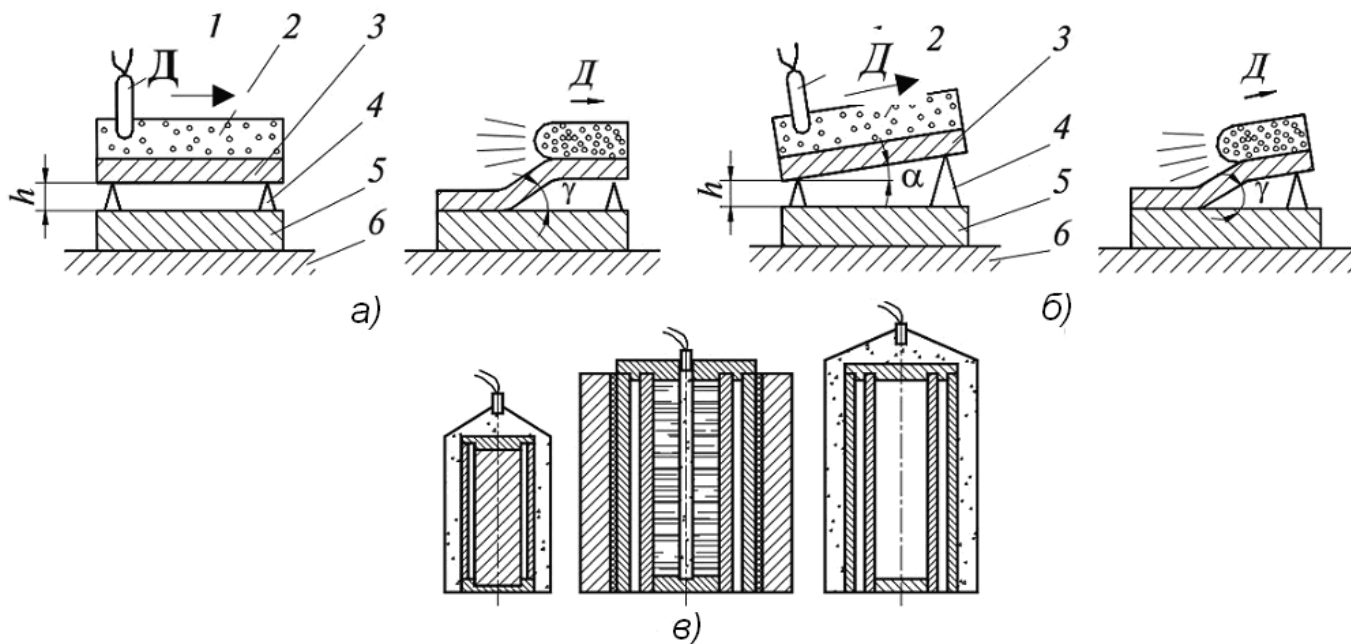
Сварка биметаллов взрывом [1]: а – параллельная схема сварки; б – угловая схема сварки; в – сварка цилиндрических обечаек. 1 – детонатор; 2 – заряд взрывчатого вещества; 3 – метаемая пластина; 4 – установочный элемент; 5 – основная пластина; 6 – основание
